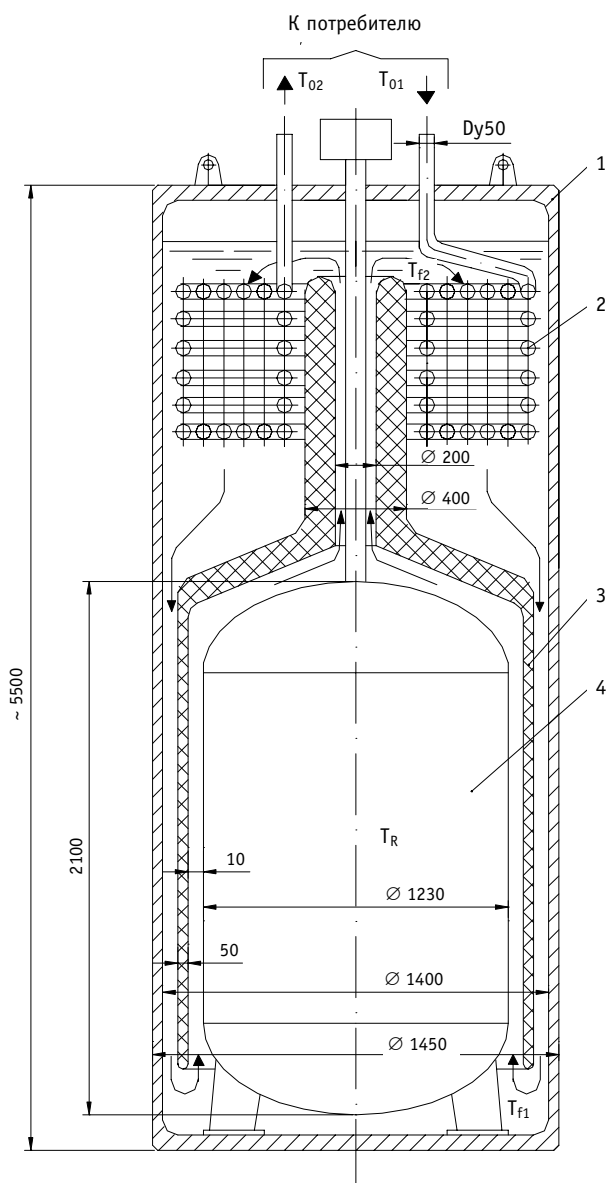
Конструктивная схема реакторной установки: 1 - корпус; 2 - теплообменная поверхность; 3 - разделительная обечайка; 4 - реактор
